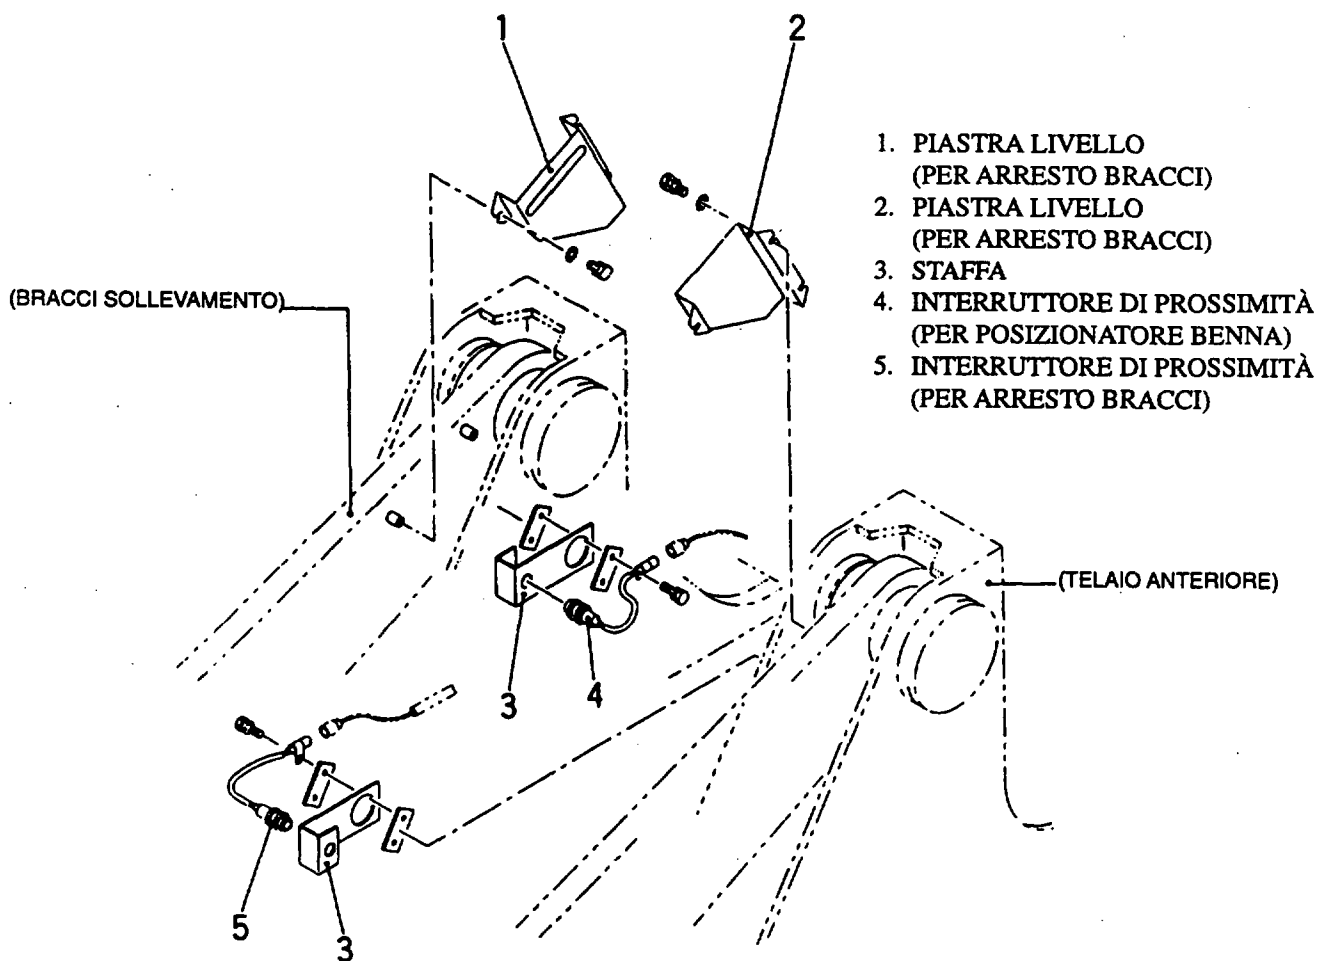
Arresto bracci sollevamento e posizionatore benna
